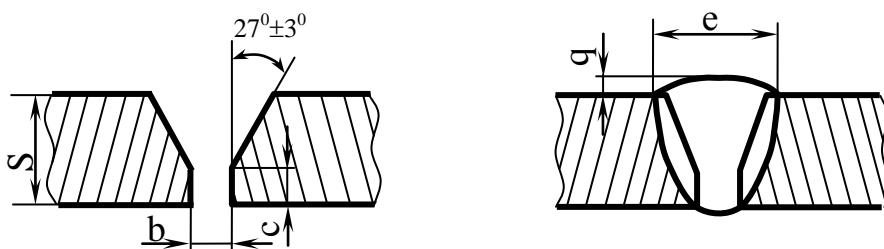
Сварное соединение до и после сварки
